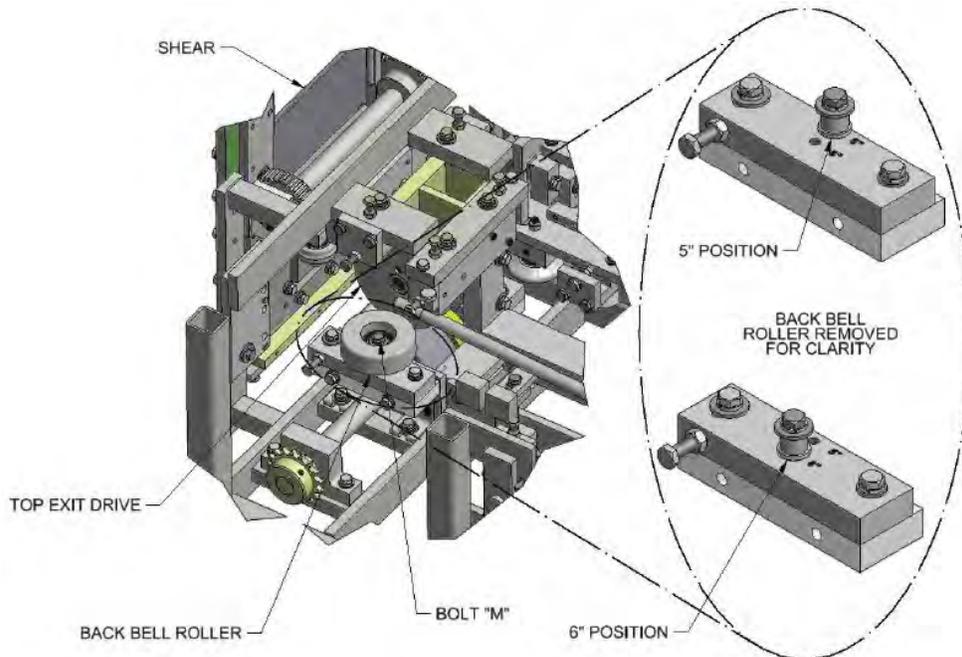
Ajuste del ensamble (bead assembly) en la máquina combo
